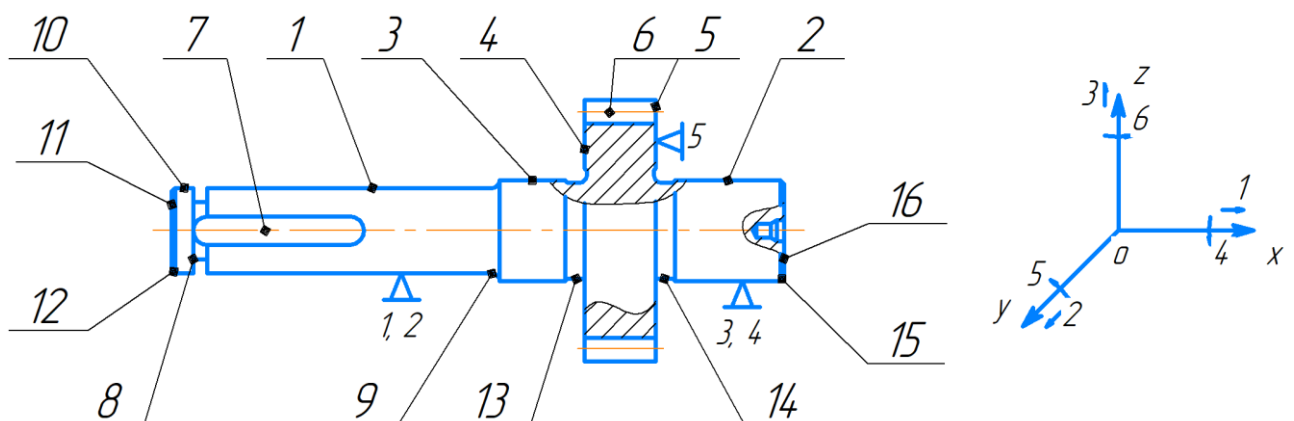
Ескіз деталі «Вал-шестірня»
